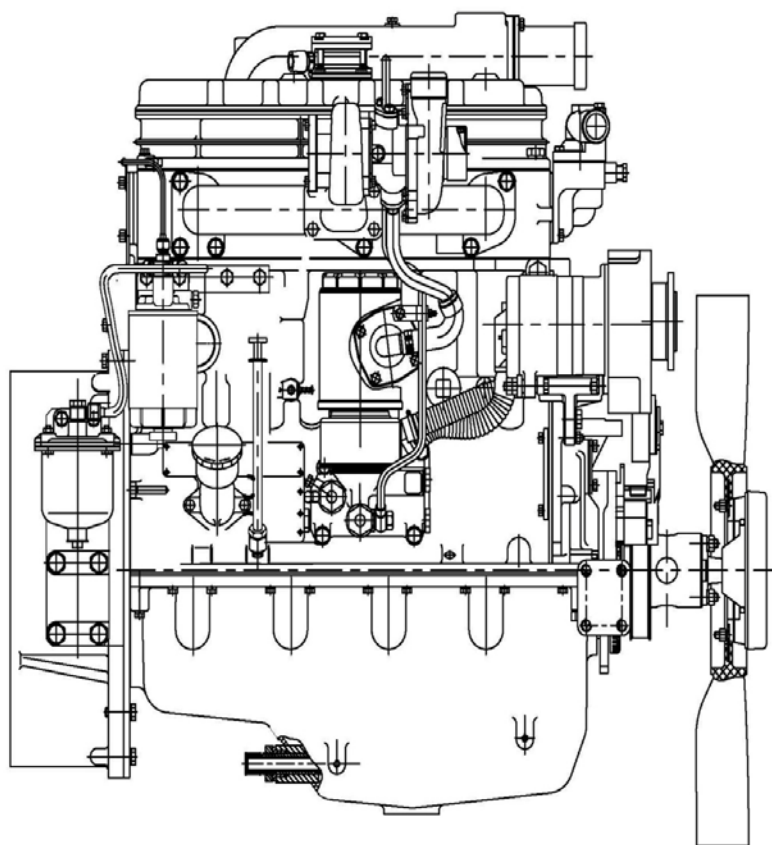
Общий вид двигателя Д-246.10, Д-246.11.
